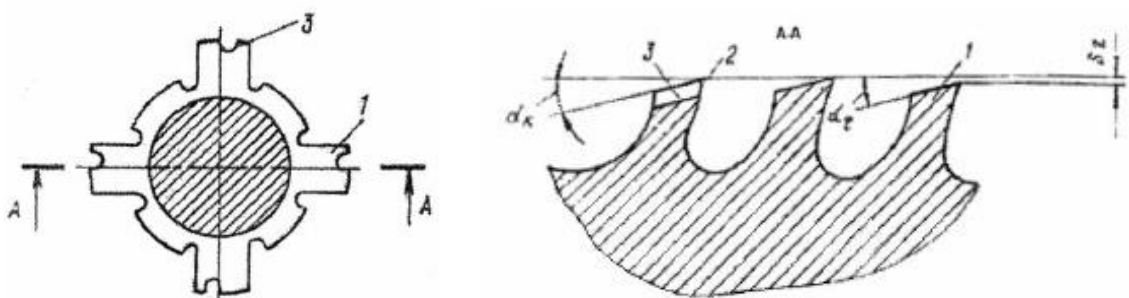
Протяжка для швидкісної обробки [8]
